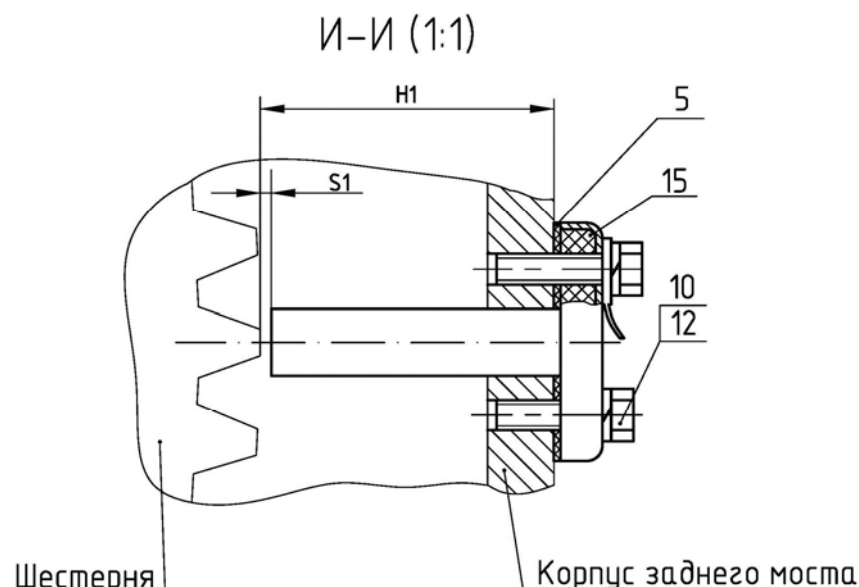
Установка и регулировка датчика оборотов ВОМ.
